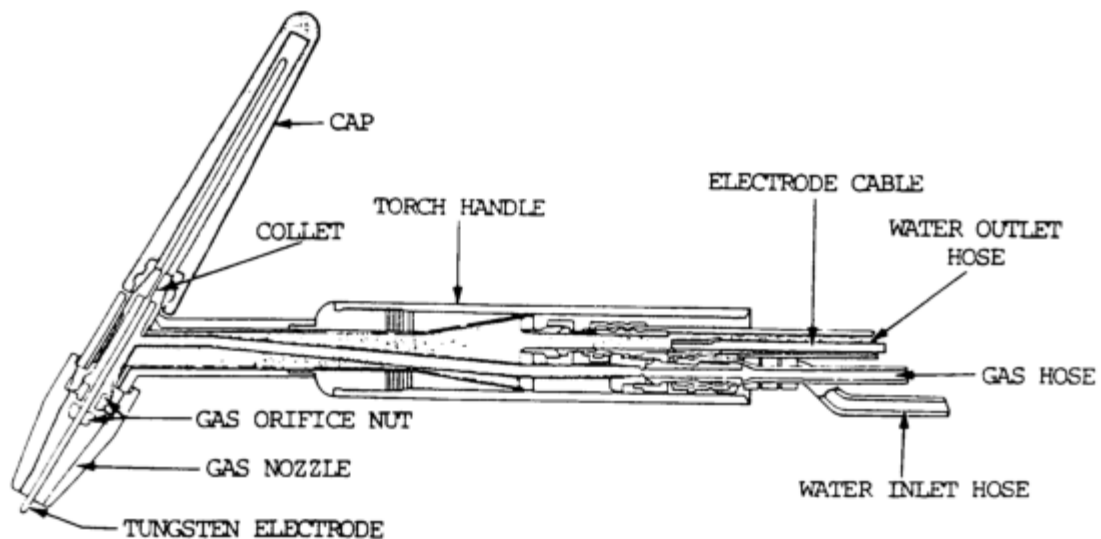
Tocha de soldadura TIG [1].
